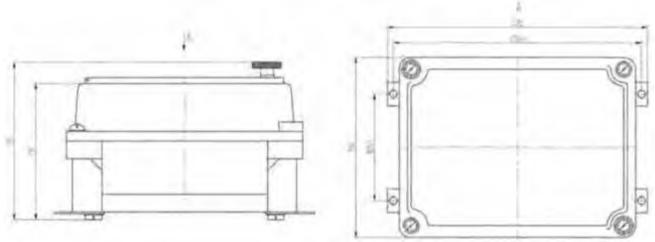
Габаритные и установочные размеры блока искрозащиты в алюминиевом корпусе
